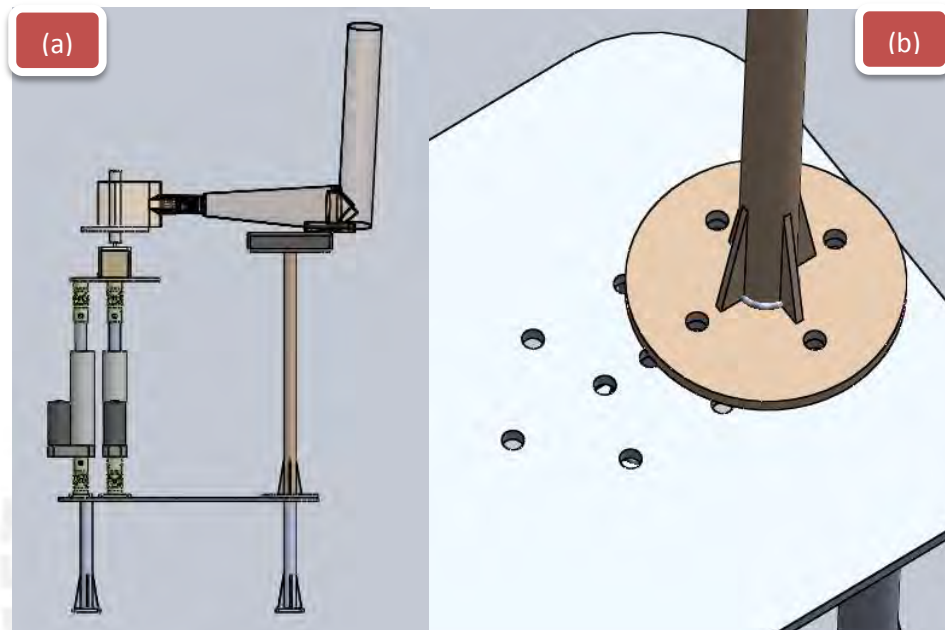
(a) Ensamble entre los tornillos y la plataforma horizontal. (b) Disposición del desplazamiento del soporte del brazo.
